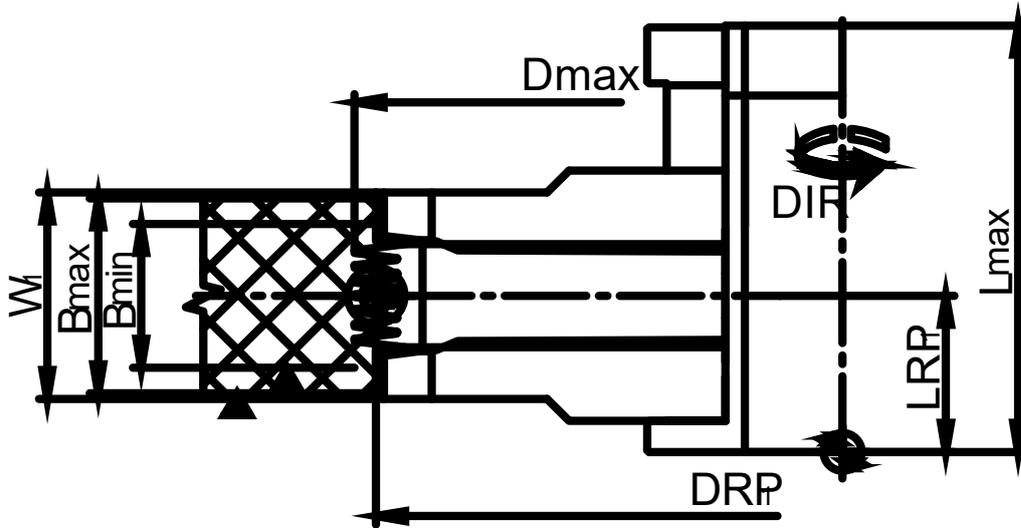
Maßdefinition für Keilzinkenwerkzeuge ohne Randzinken
